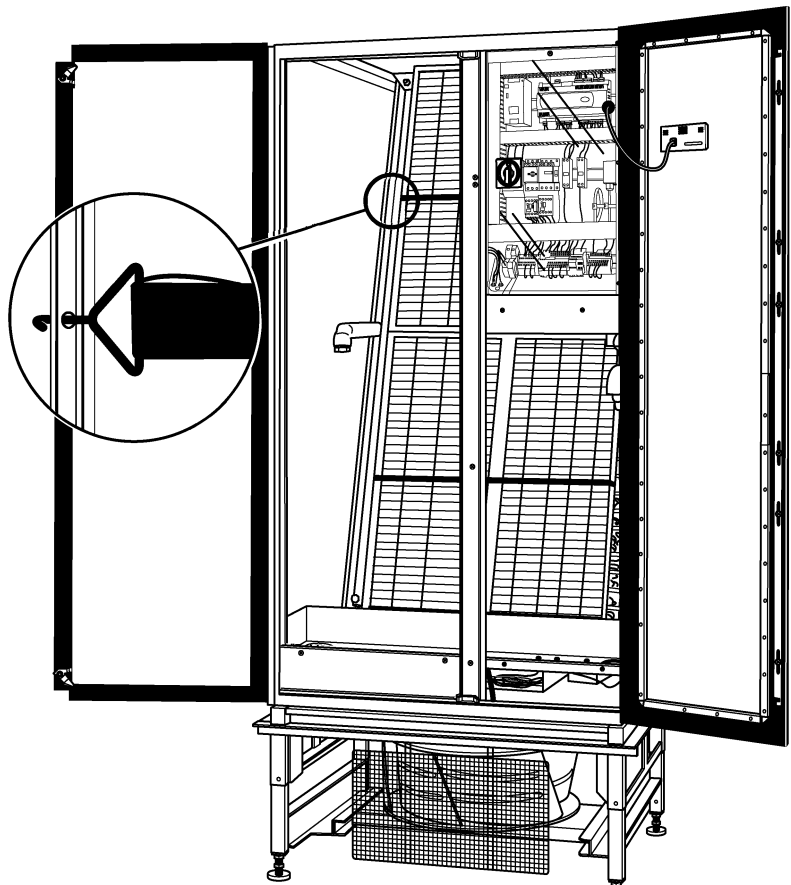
Filterbefestigung mit Spanngummi (hier: Ausführung CW)
